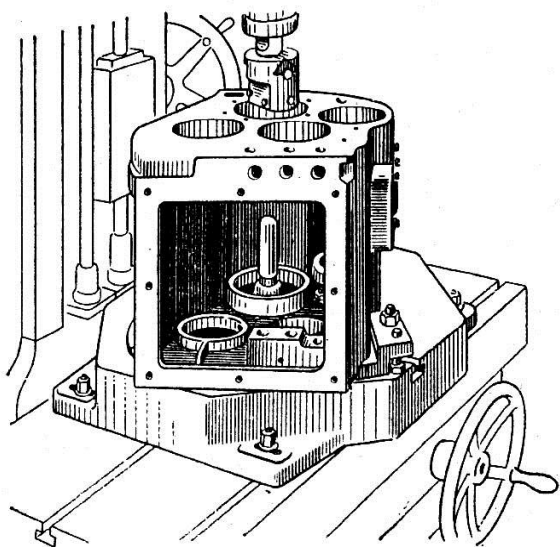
Розточування поверхні отвору в корпусі коробки передач трактора на вертикально-розточувальному верстаті 278Н.
